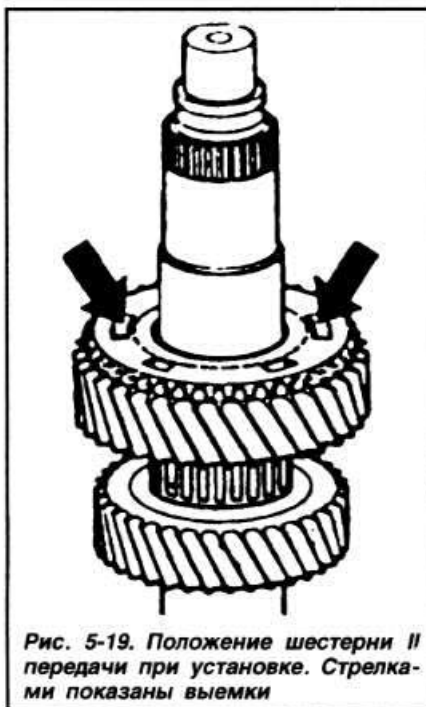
Положение шестерни II передачи при установке. Стрелками показаны выемки
